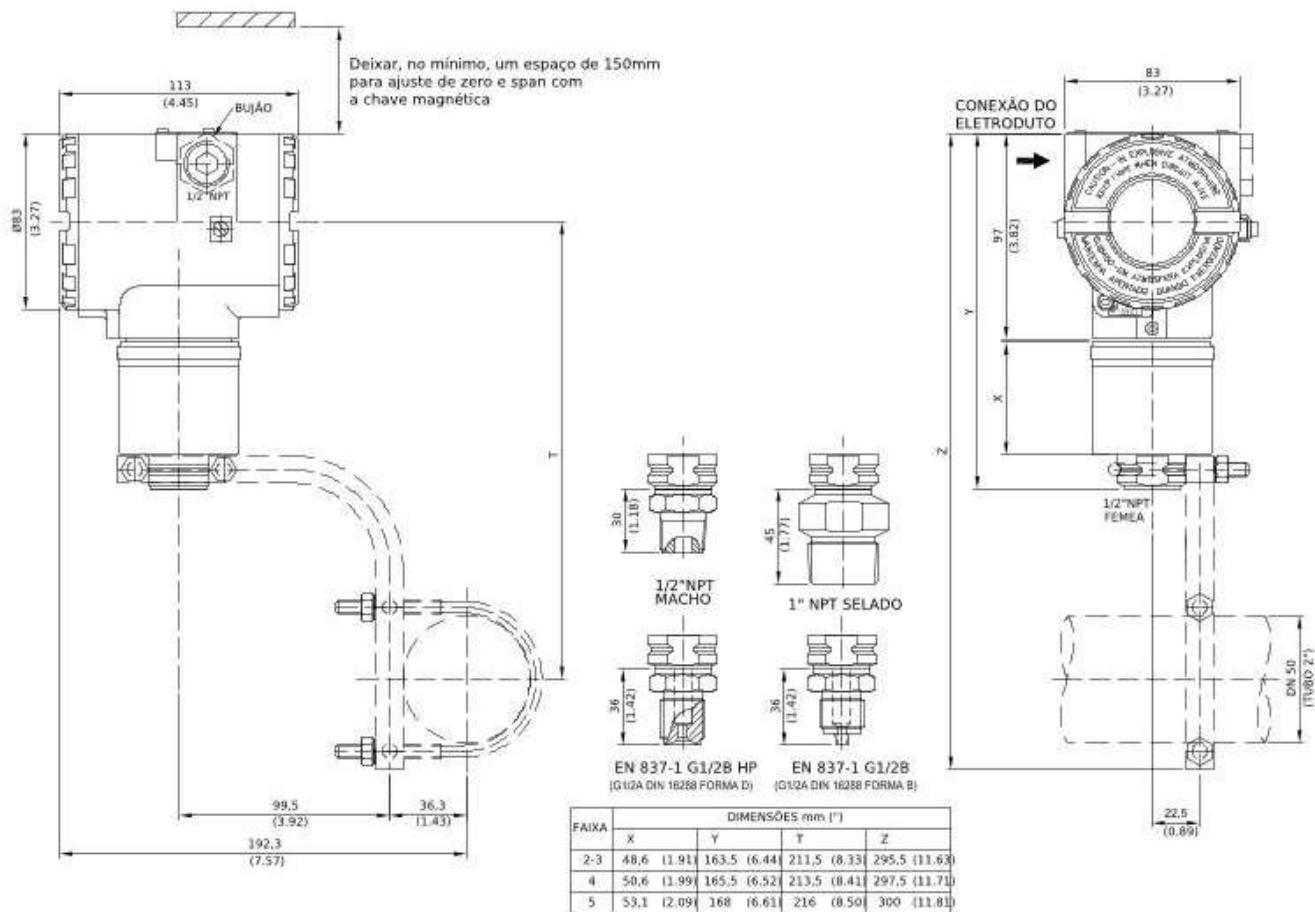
(a) - Desenho Dimensional e Posição de Montagem para o LD293 - Transmissor com Suporte de Montagem
